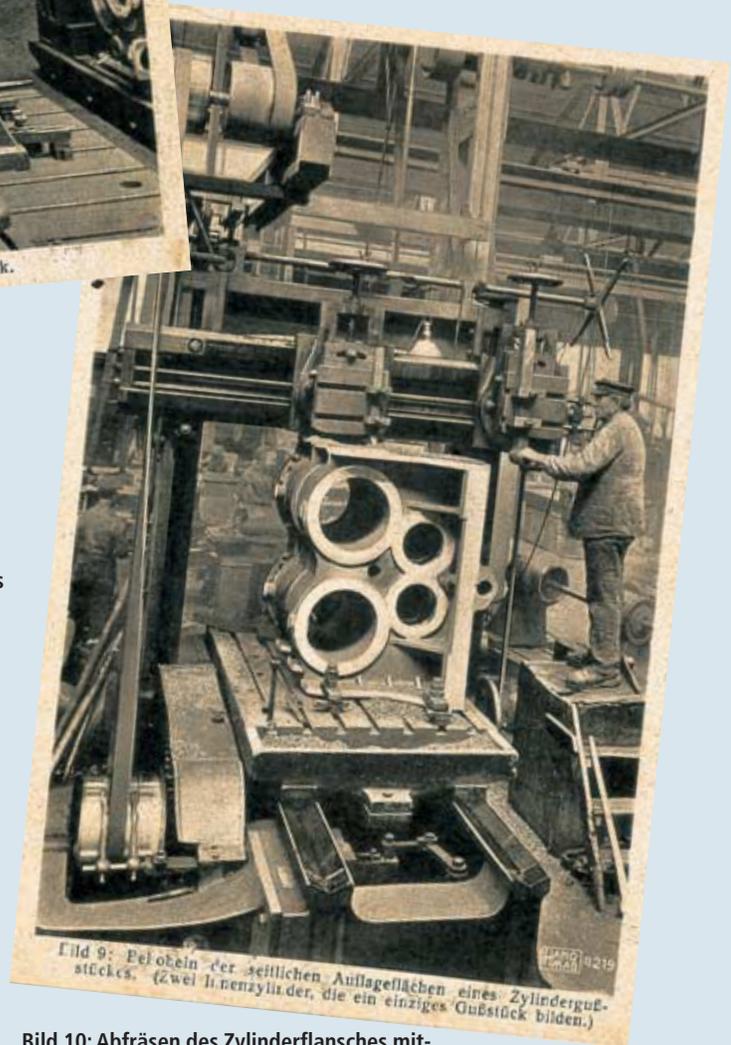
Behalten der seitlichen Auflageflächen eines Zylindergußstückes. (Zwei Innenzylinder, die ein einziges Gußstück bilden.)
